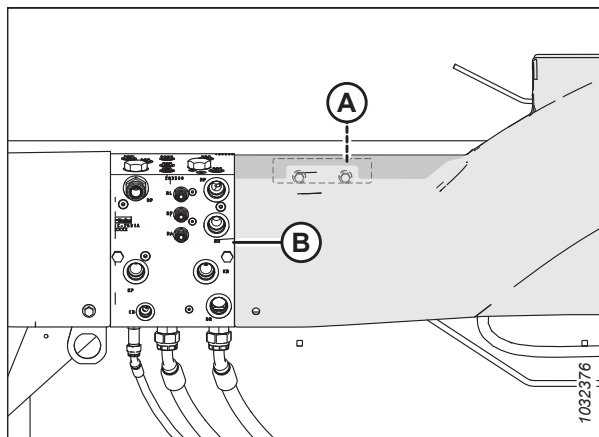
Levý kryt spojovacího ústrojí – zadní část adaptéru
